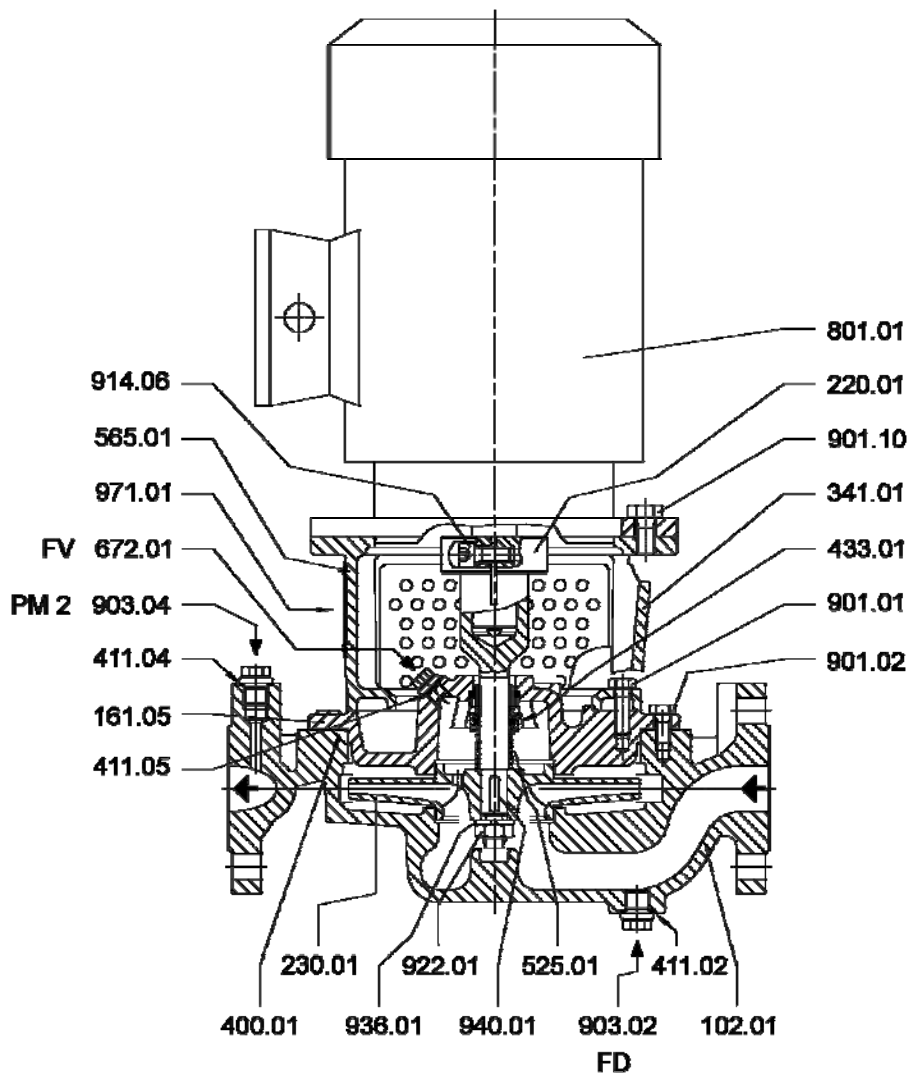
U3...D – Торцевое уплотнение под нагрузкой – типоразмер с диаметром 16 на уплотнении вала
